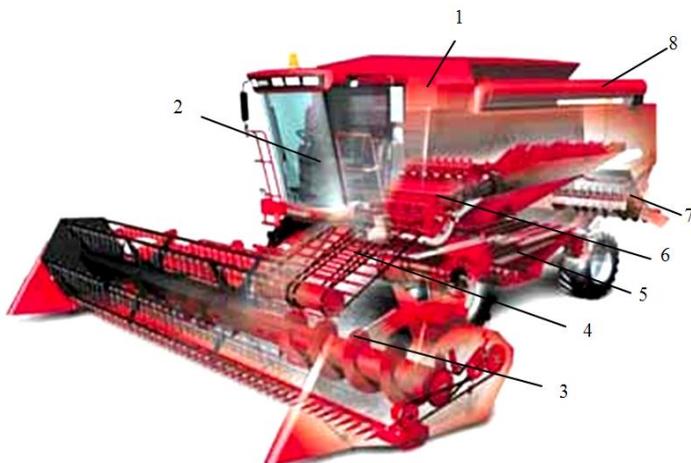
зерноуборочный комбайн «Лиди-1600»:
